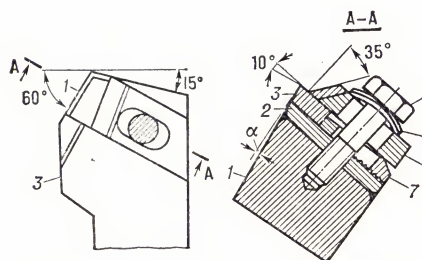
Резец конструкции ЦНИИТМаш с механическим закреплением пластинки: 1 — державка; 2 — подкладка; 3 — пластина; 4 — болт; 5 — шайба; 6 — прижим; 7 — передвижной упор.
